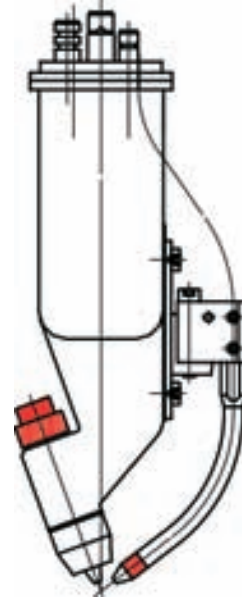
Plasmabrenner mit integrierter Kaltdrahtzuführung
